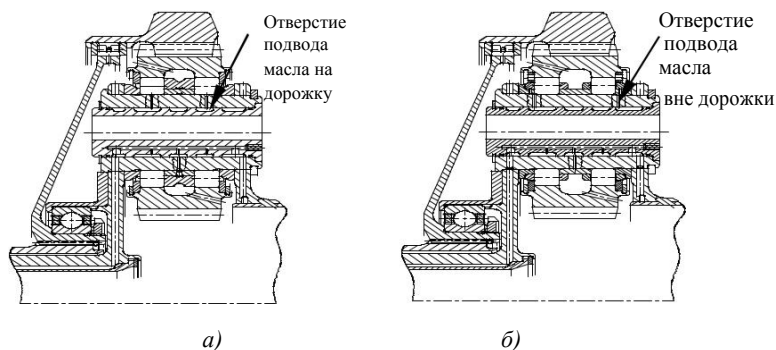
Схема подвода смазки в подшипники главного редуктора двигателя ТВ3-117ВМА-СБМ1: – исходная конструкция; б – доработанная конструкция подшипника сателлита
